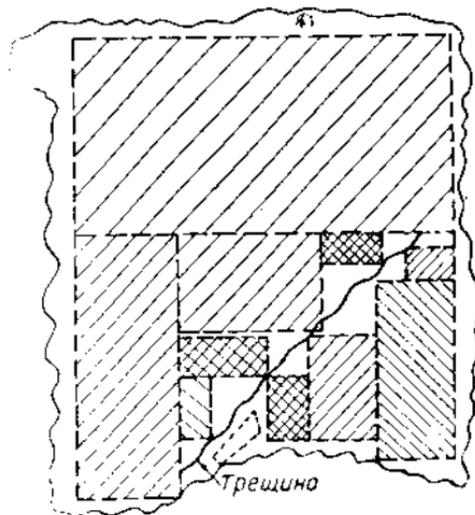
Разметка дефектной каменной доски для фрезеровки с наименьшими отходами
